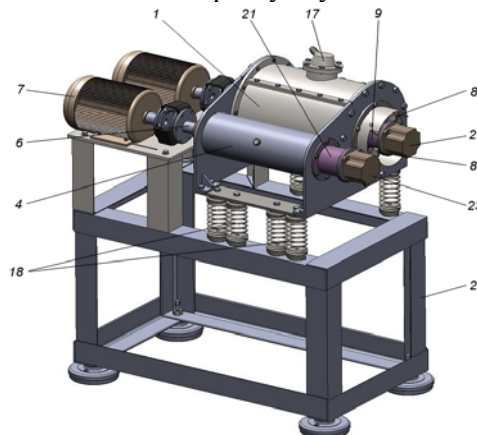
Загальний вигляд запропонованого пристрою для віброабразивної обробки деталей у автоматичному режимі (вигляд із сторони контейнера)
